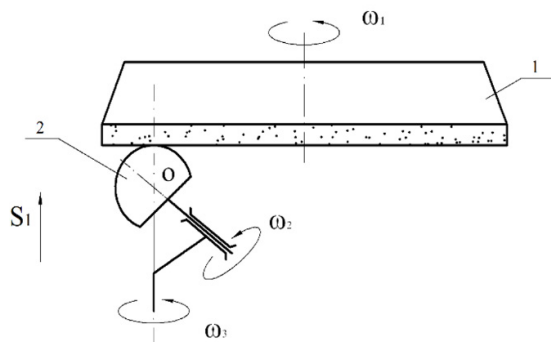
Схема формообразования неполной сферической поверхности торцевым алмазным кругом с двойным вращением детали: 1 – алмазный шлифовальный круг; 2 – обрабатываемая деталь – неполная сфера
